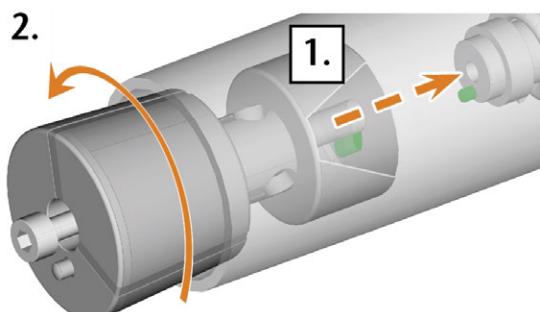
INSERIMENTO DELLA PINZA DI SERRAGGIO NEL PORTAPEZZI
